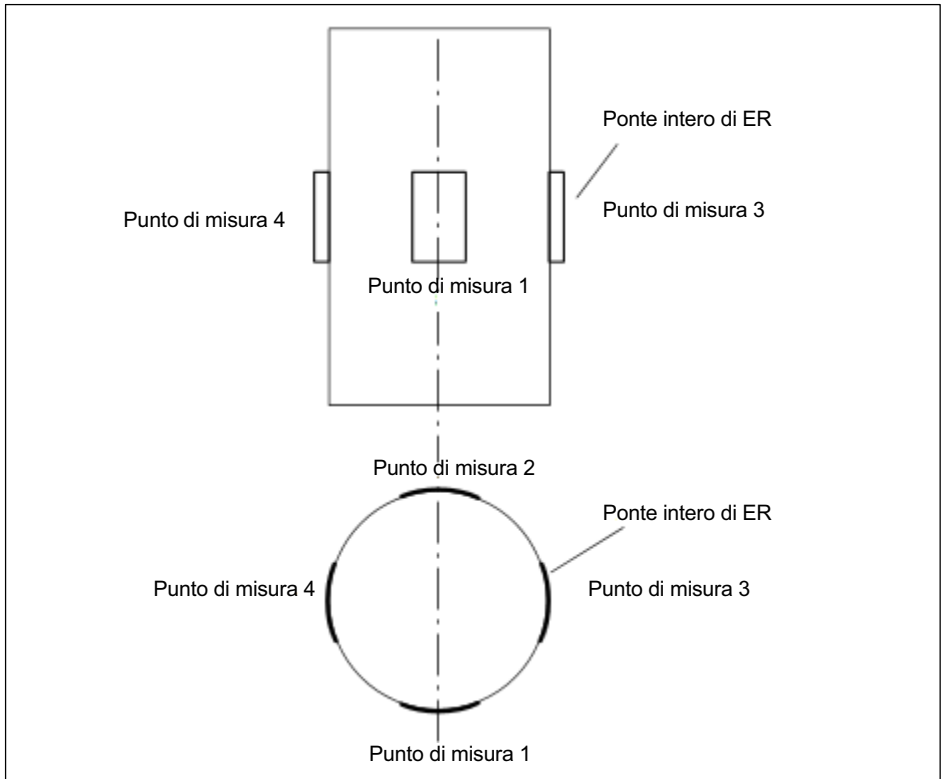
Installazione dei 4 ponti interi di ER sul perimetro del corpo di misura
